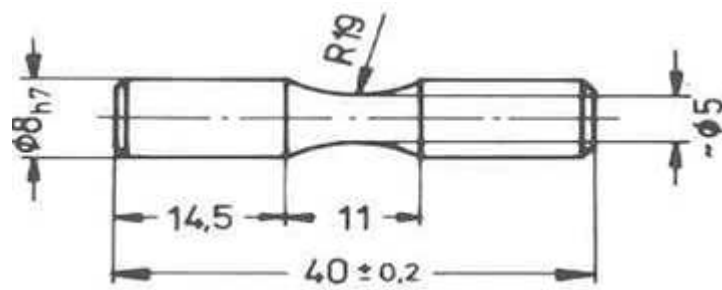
Dimensions des éprouvettes « Small sized test sample »
